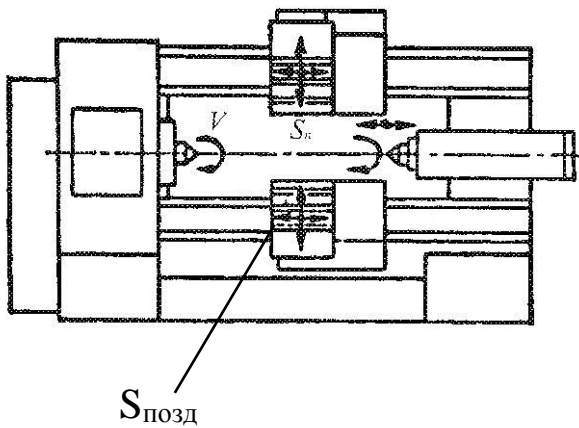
Загальний вид токарного багаторізцевого напівавтомата
